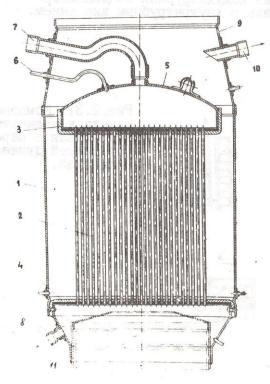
Бесфланцевый кожухотрубный конденсатор-испаритель. І-обечайка; 2-трубка; 3,4-коллекторы; 5-крышка; 6- продувка; 7-сброс давления; 8,9 - переходные конуса; 10-отбор кислорода; II - слив азота.
